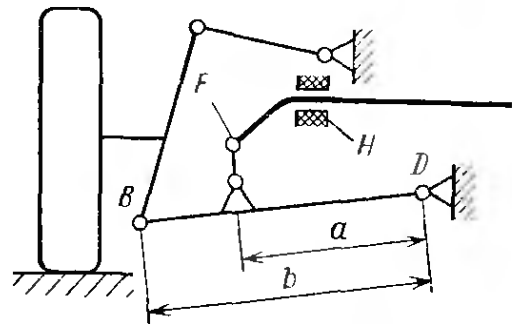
Стабилизатор типа 2 своей центральной частью шарнирно закреплен в точках H . Концы F стабилизатора соединены с поперечными рычагами через промежуточные тяги
